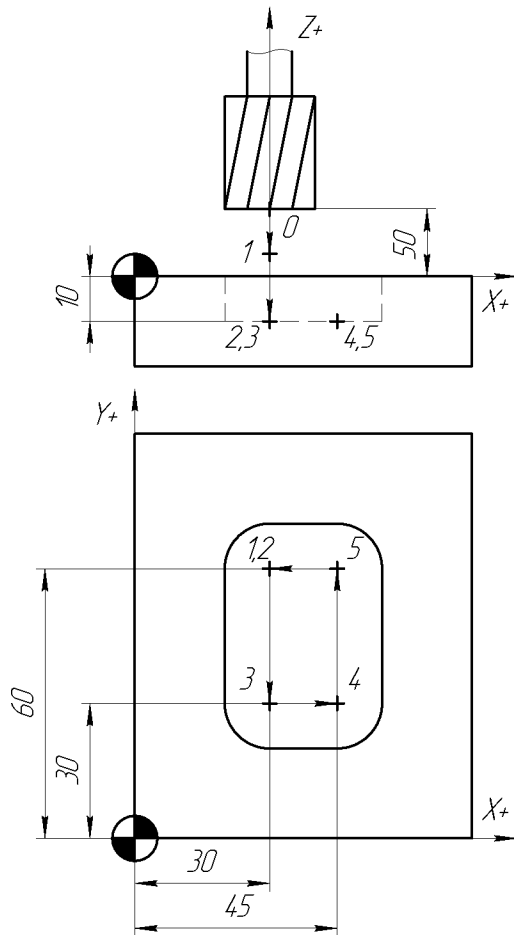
Циклограма обробки деталі на фрезерному верстаті з ЧПК
